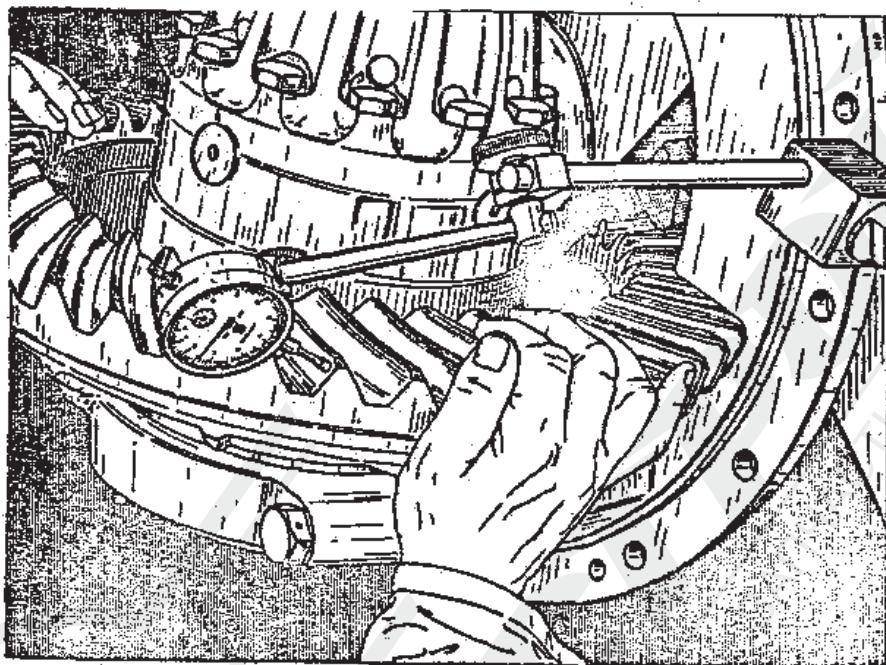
Примерка зазора между зубьями приводного и та-
